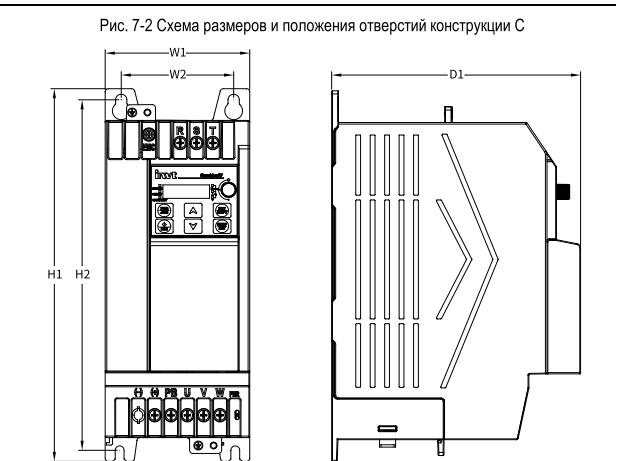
Схема размеров и положения отверстий конструкции С
